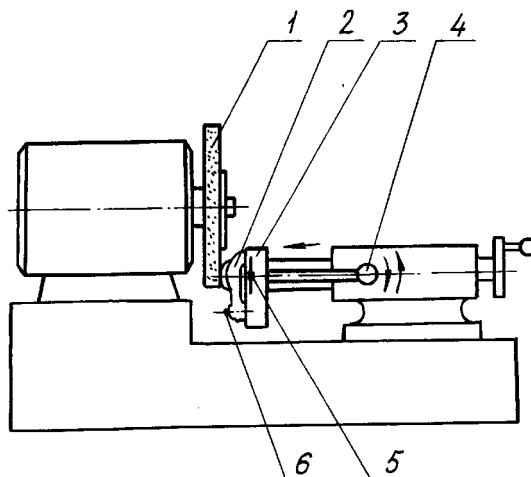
Станок для шлифования рычагов привода клапанов:
